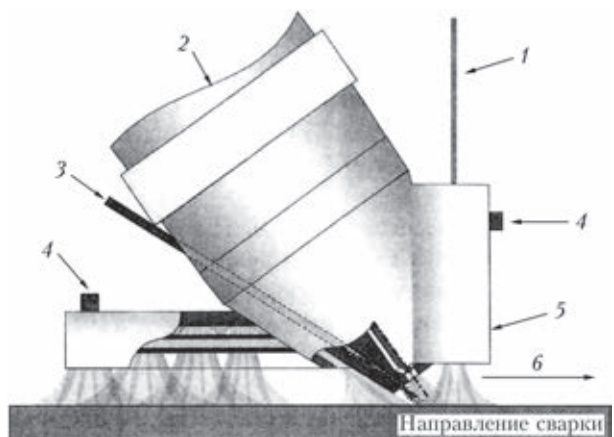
Схема гибридной лазерно-плазменной сварки с плазменной дугой прямого действия и порошковой присадкой [17]: 1 — лазерное излучение; 2 — плазмообразующий газ; 3 — порошок с транспортирующим газом; 4 — защитный газ; 5 — трубка, через которую подается излучение; 6 — направление сварки
